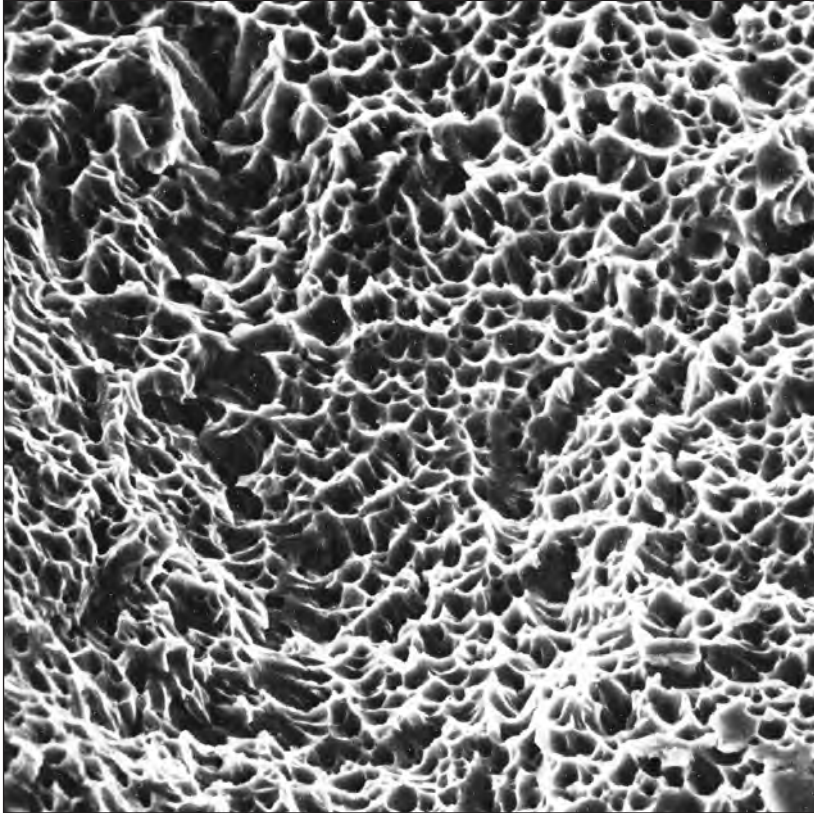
Gerade Waben im Rest-Gewaltbruch einer Stahlfeder.
